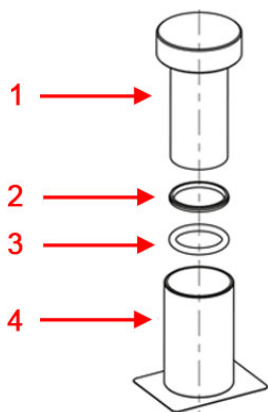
O-Ring in das Montagewerkzeug einsetzen
